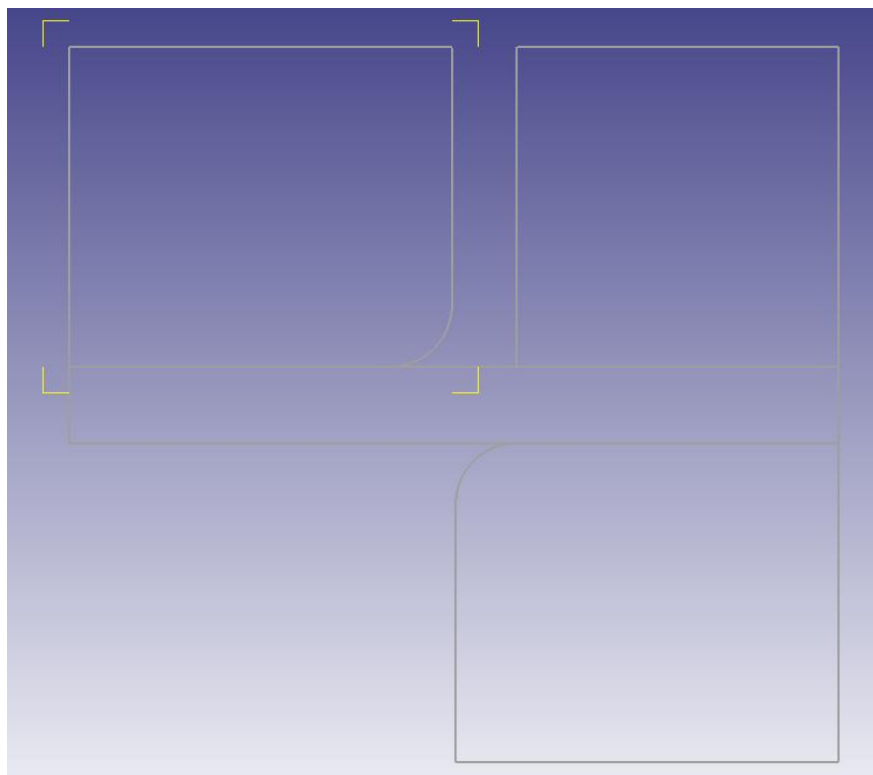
Геометрия рабочих частей штампов и заготовки
